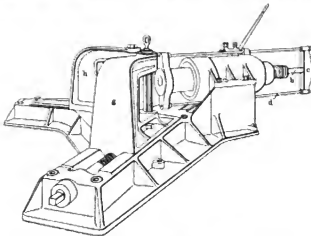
Z. A.: Hydraulische Rohrbiegemaschine.
